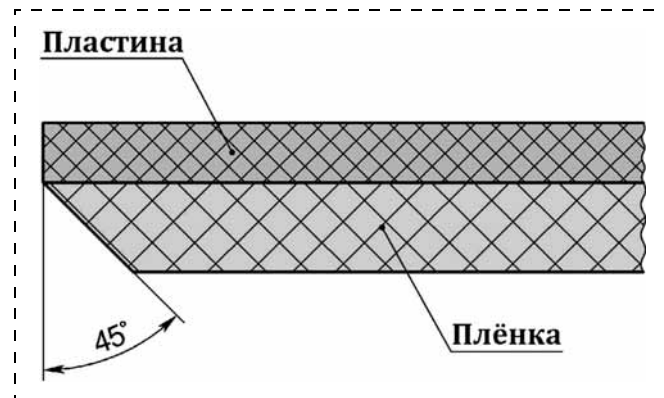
Обрезка пленки под углом 45° к поверхности пластины
